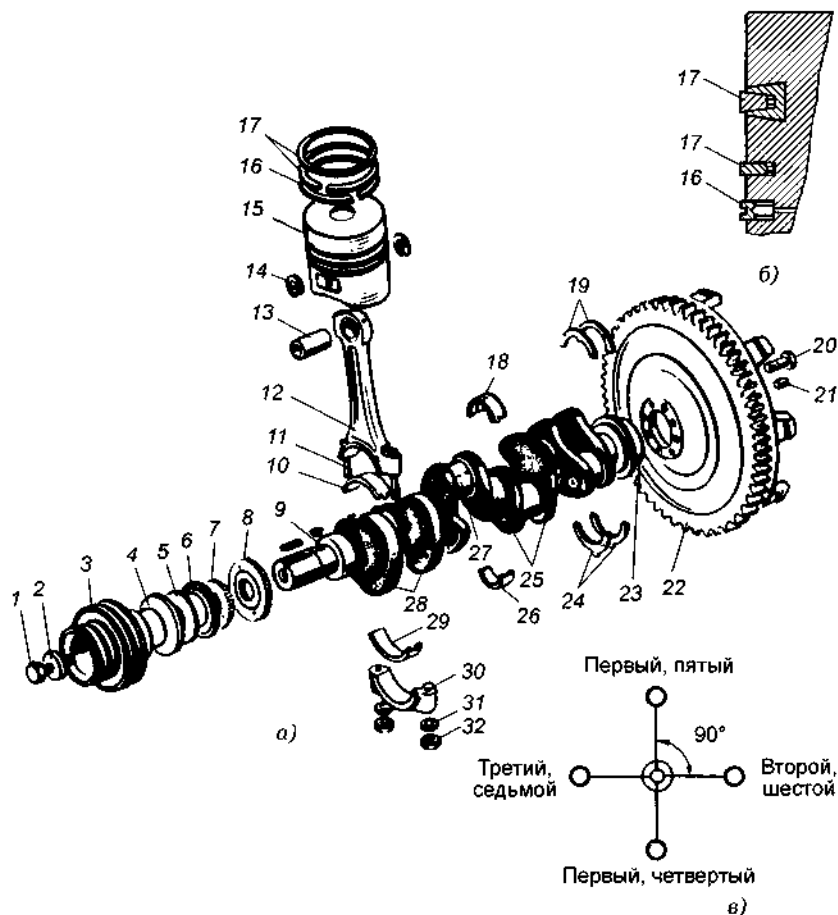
Кривошипно-шатунный механизм (а), расположение колец (б) и схема расположения шатунов (в): 1 — болт; 2 — шайба; 3 — шкив; 4 — пылеотражатель; 5 — кольцо манжеты; 6 — маслоотражатель; 7 — распределительное зубчатое колесо; 8 — зубчатое колесо привода масляного насоса; 9 — коленчатый вал; 10 и 29 — вкладыши подшипников нижней головки шатуна; 11 — шатунный болт; 12 — шатун; 13 — поршневой палец; 14 — стопорное кольцо; 15 — поршень; 16 — маслосъемное кольцо; 17 — компрессионные кольца; 18 и 26 — подшипники коленчатого вала; 19 и 24 — упорные подшипники коленчатого вала; 20 — болт крепления маховика; 21 — штифт; 22 — маховик; 23 — фланец крепления маховика; 25 — коренные шейки; 27 — шатунная шейка; 28 — противовесы; 30 — крышка шатуна; 31 — шайба; 32 — гайка
